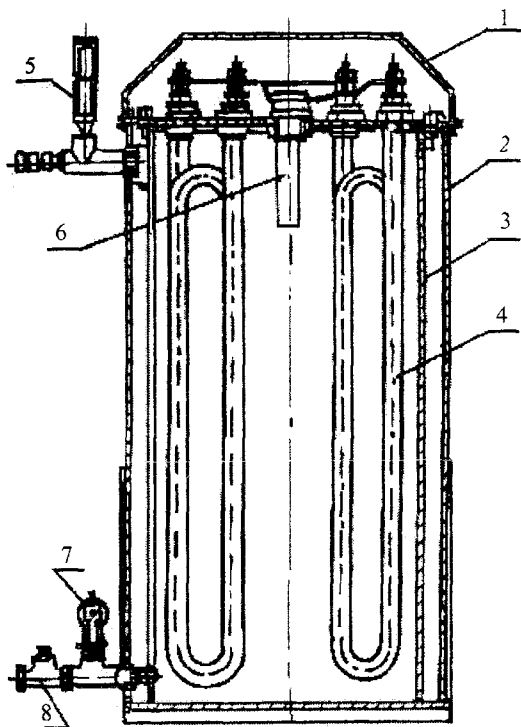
Водонагреватель ЭВ-Ф-15: 1 – крышка; 2 – кожух; 3 – корпус; 4 – трубчатые нагреватели; 5 – термометр; 6 – термореле защиты нагревателей от перегрева; 7 – клапан избыточного давления; 8 – обратный клапан
